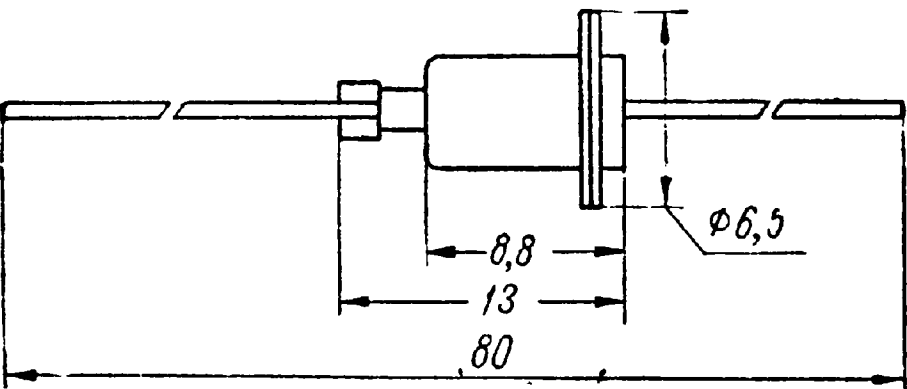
Основные размеры и схематическое изображение стабилитронов 2С156А и 2С168А.
